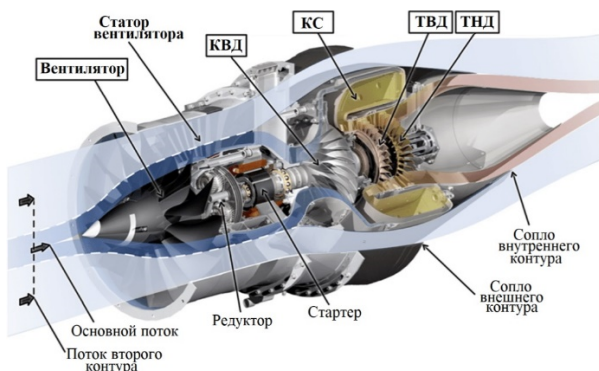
Малоразмерный ТРДД DGEN-380
